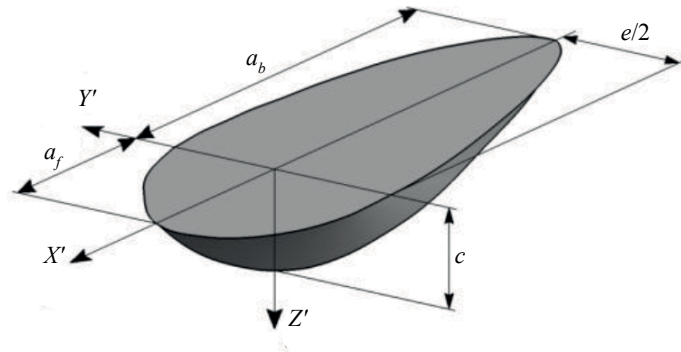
Размеры источника нагрева (сварочной ванны).
